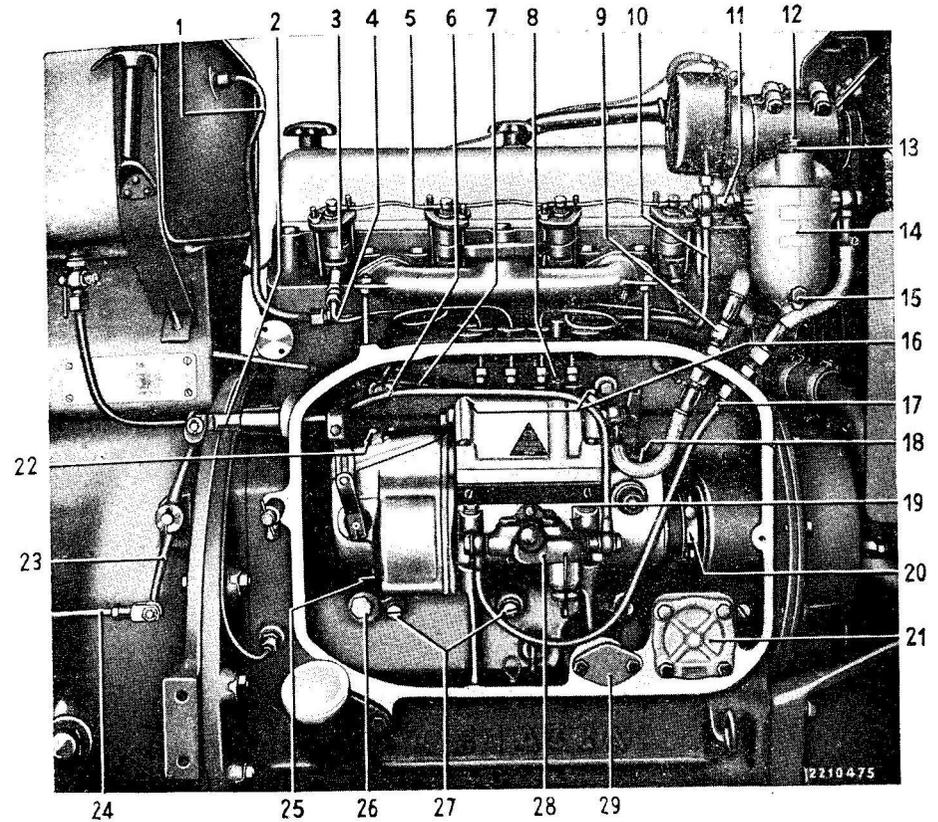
Kraftstoffanlage mit Einspritzpumpe „Bauart Deckel“
